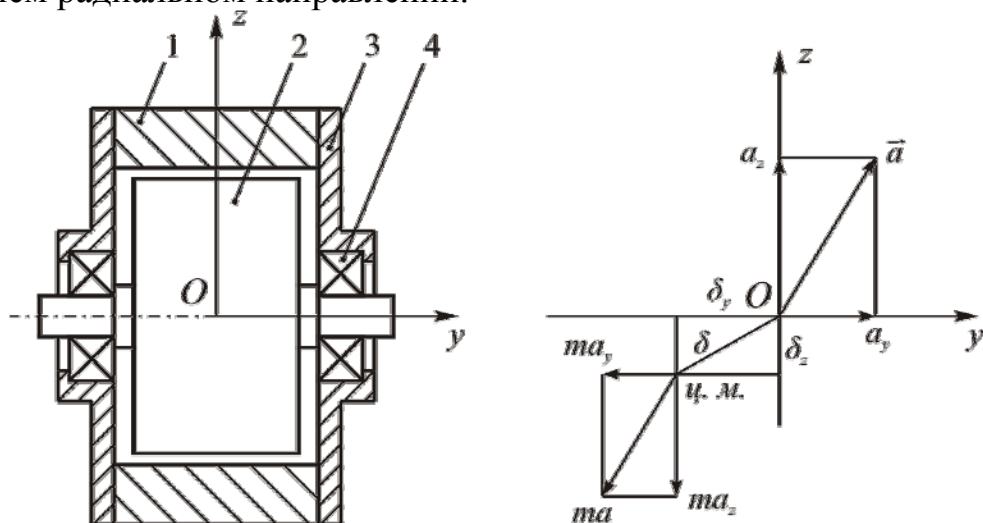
Конструктивная схема гиросмотора и схема сил инерции, приложенных к центру масс: 1 – ротор; 2 – статор; 3 – крышка; 4 – подшипник
